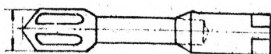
развертка напильтная с цилиндрическим хвостовиком
